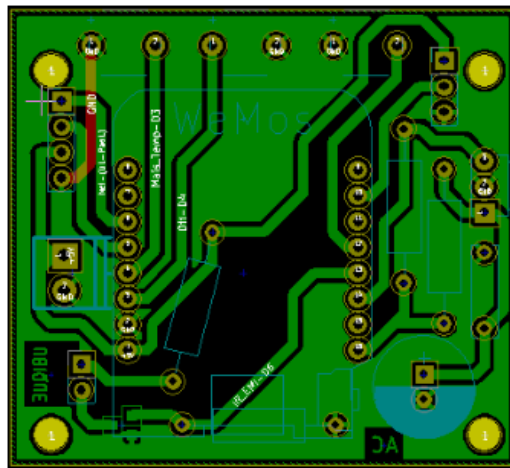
Layout da placa de circuito impresso, disposto dos componentes e rotas. Fonte: Próprio Autor
